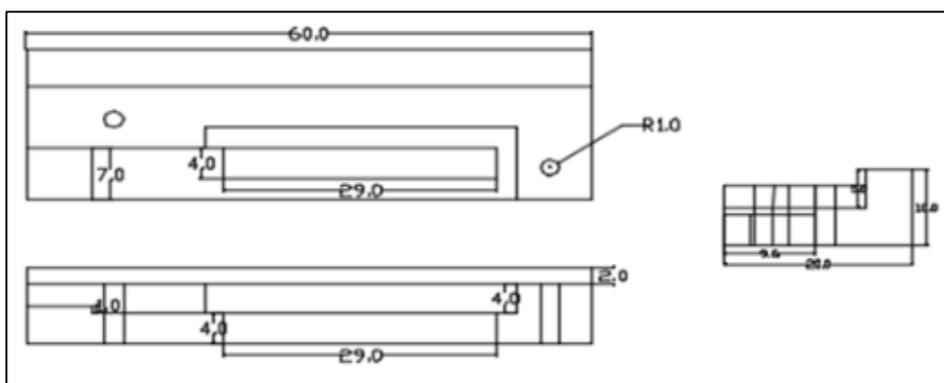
Desenho em CAD do suporte periférico para conector USB.
